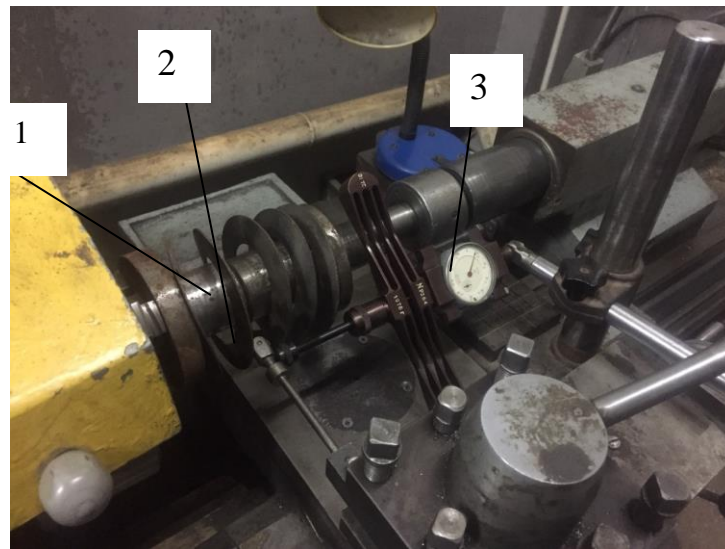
Загальний вигляд експериментальної установки для калібрування гвинтових заготовок: 1 – гвинтова заготовка; 2 - клин для здійснення калібрування гвинтової заготовки; 3 - динамометр
